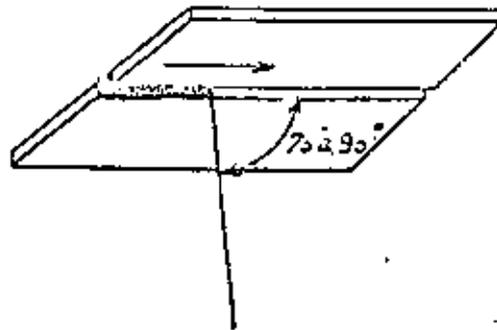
FIG. V-II.- METODO DE SOLDADURA EN TECHO.
